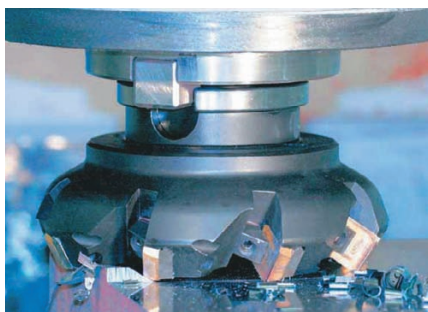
Фреза для черновой обработки с пластинами SBMR 22
